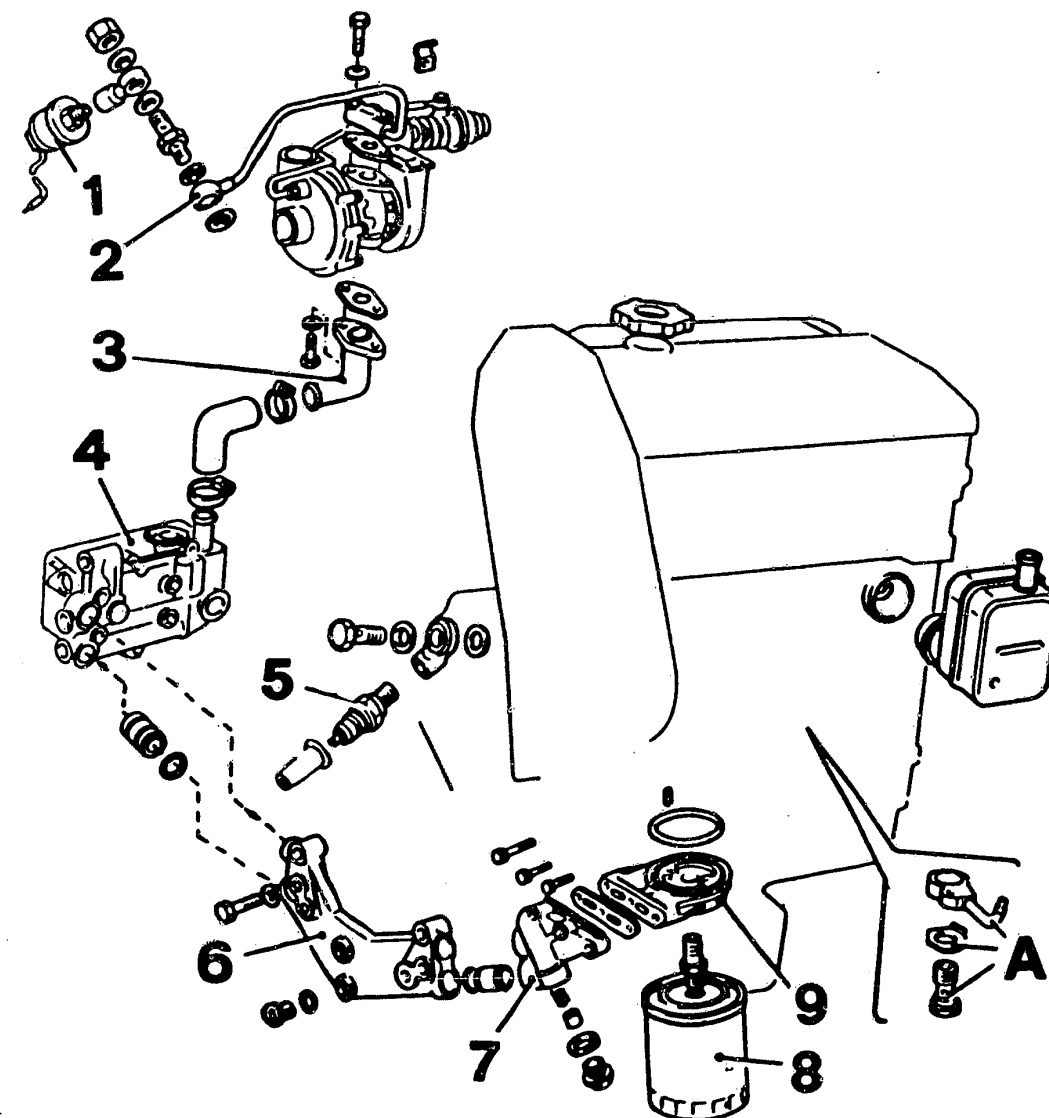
Die äusseren Teile des Schmiersystems am 2500 Turbo-Dieselmotor: 1 Öldruckgeber – 2 Zufuhrleitung zum Turbolader – 3 Schlauchanschluss zwischen Turbolader und Wärmeaustauscher (4) – 5 Öldruckschalter – 6 Verbindungsteil – 7 Sicherheitsventil – 8 Ölfilter – 9 Befestigungsflansch – A Spritzrohr im Kurbelgehäuse zur Kühlung des Kolbenbodens.
